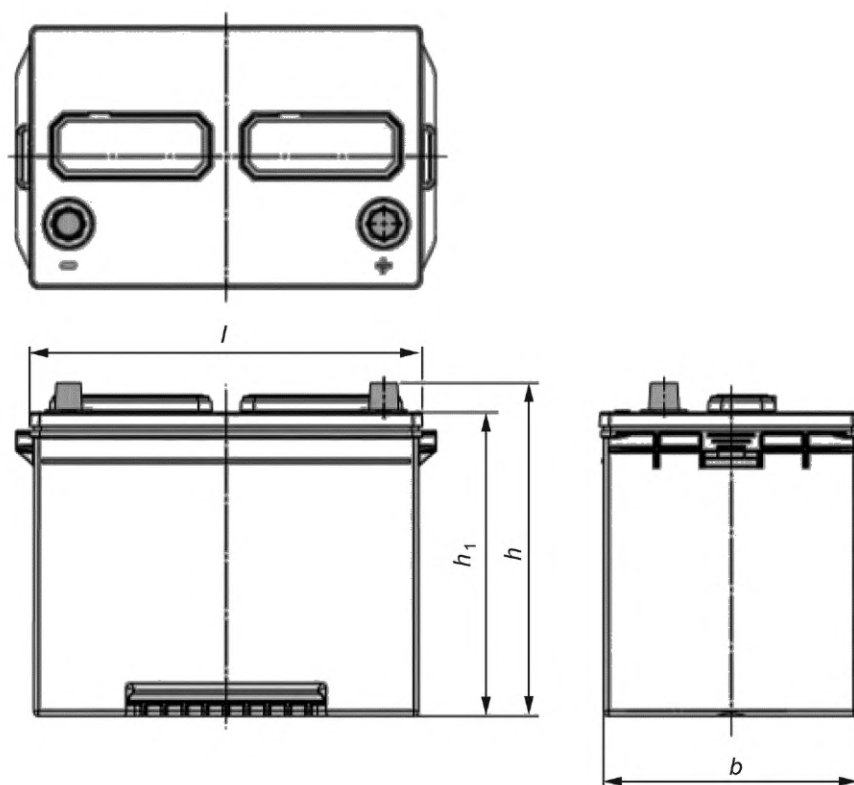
Основные размеры батарей типоразмеров 24R, 26R, 34R, 35, 51R, 85
